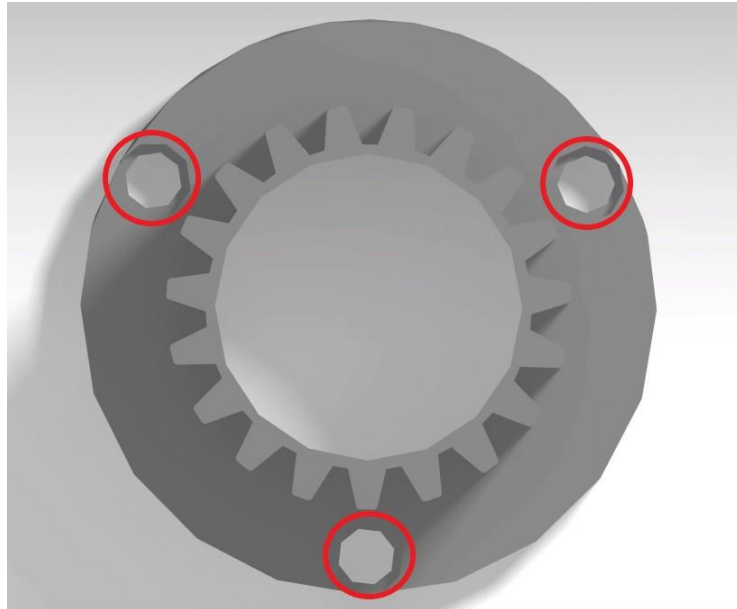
Vista en detalle del TALADRADO del piñón (Fuente: elaboración propia)
